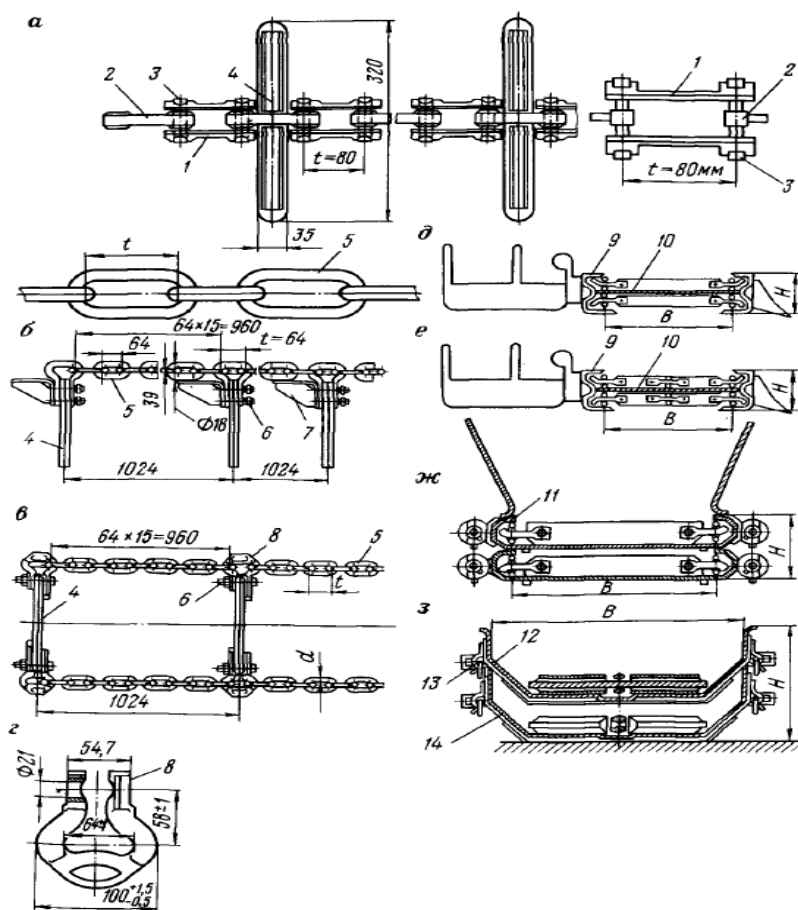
Узлы скребковых конвейеров: а – тяговая цепь со скребками штампованная; б, в – то же, круглозвенная; г – соединительное звено цепи; д, з - сечение рештачного става (д, е – конвейеров типа СП, ж – СР70 и С53); 1 – боковое звено; 2 – внутренне звено; 3 – валик звена; 4 – скребок; 5 – звено цепи; 6 – соединительный болт; 7 – кронштейн; 8 – соединительное звено; 9 – боковина рештака конвейера типа СП; 10 – днище рештака; 11 – направляющие для цепи конвейера типа СР; 12, 14 – верхний и нижний рештаки конвейера типа С53; 13
